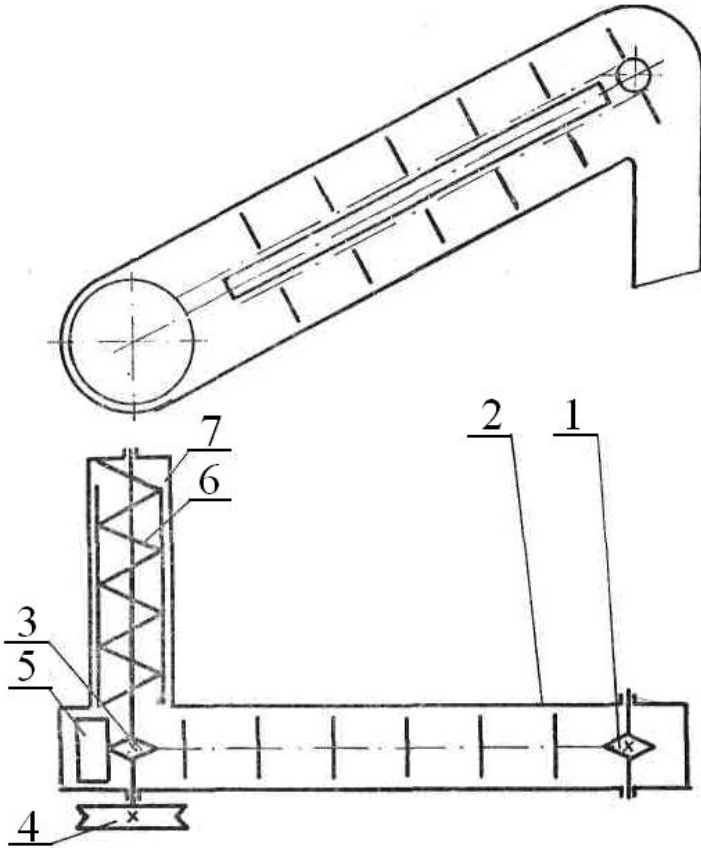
Схема похилого скребкового конвеєра: 1 – зірочка напрямна; 2 – конвеєр скребковий; 3 – зірочка ведуча; 4 – шків приводу; 5 – скребок; 6 – гвинт; 7 – живильник гвинтовий
